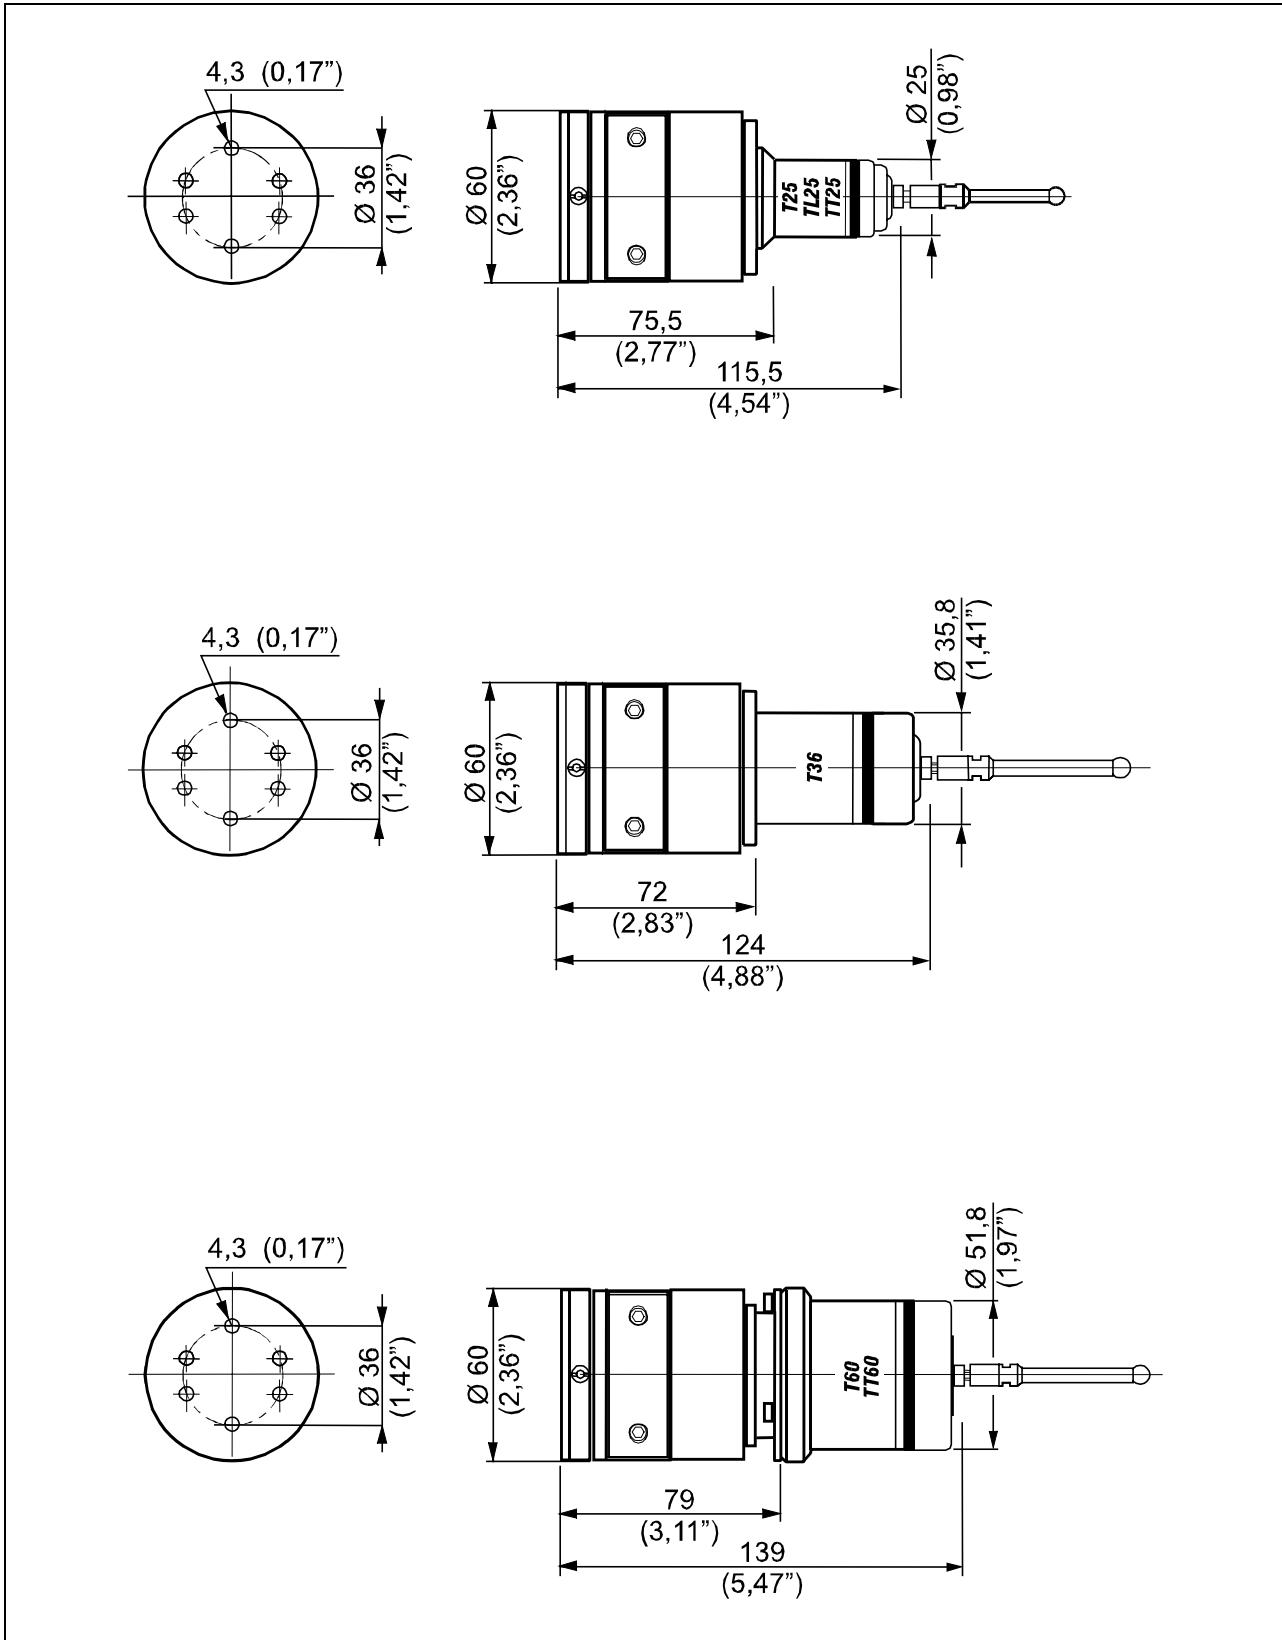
Dimensions hors tout émetteur avec flasque réglable
